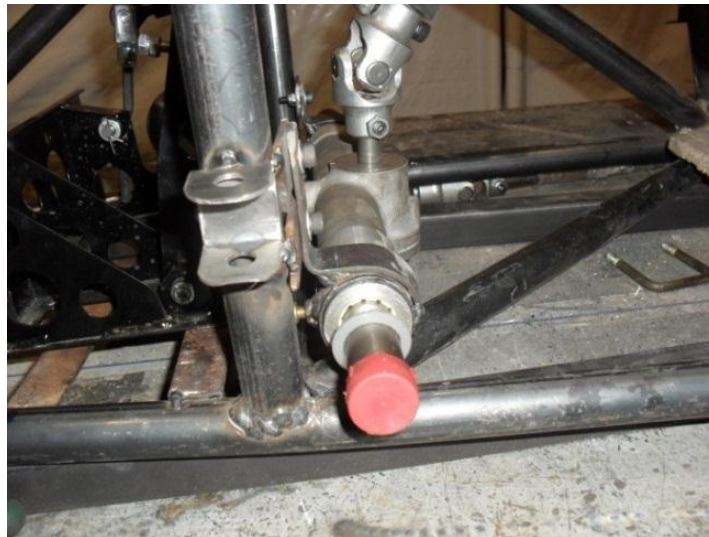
Base de Suspensión Delantera pre soldada
